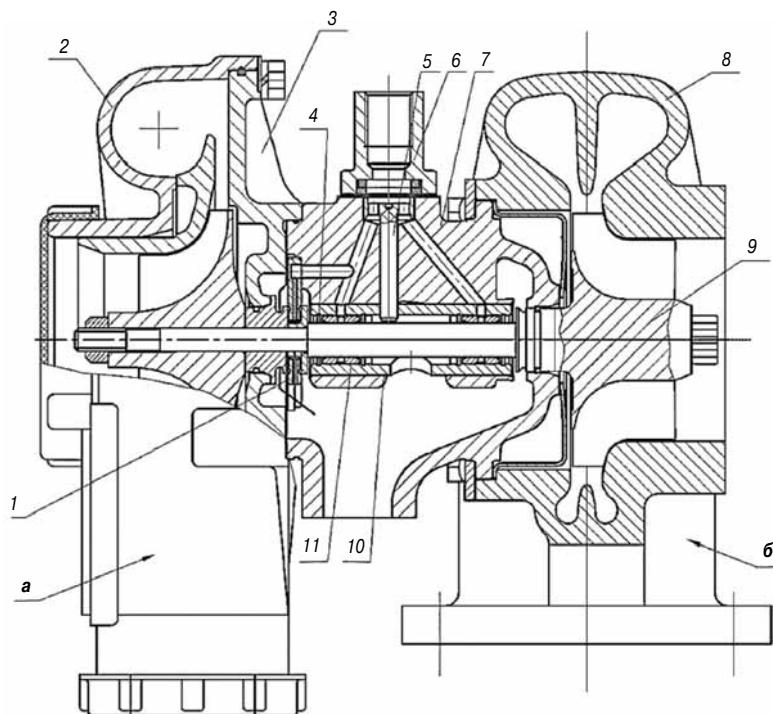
Трбокомпрессор ТКР 7С-6 с модульным подшипником:
